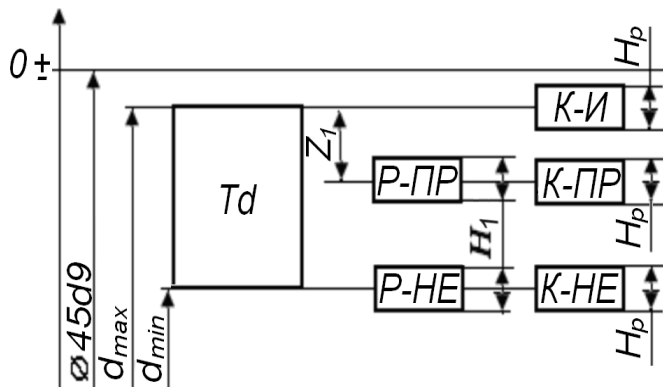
Схема розташування полів допусків контрольованого вала
